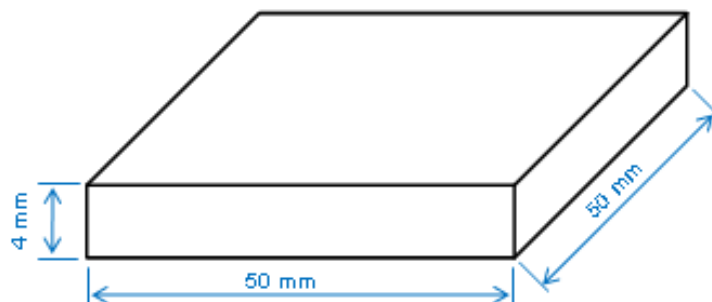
Dimensions des échantillons pour mesures par gravimétrie
